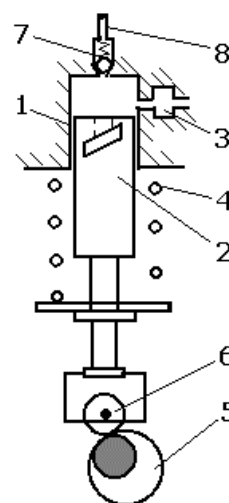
Funcționarea pompei de injecție în linie: 1 – cilindru; 2 – pistonas; 3 – colector de alimentare; 4 – arc de readucere; 5 – arbore cu came; 6 – tachel cu rolă; 7 – supapă de refulare; 8 – racord de refulare
